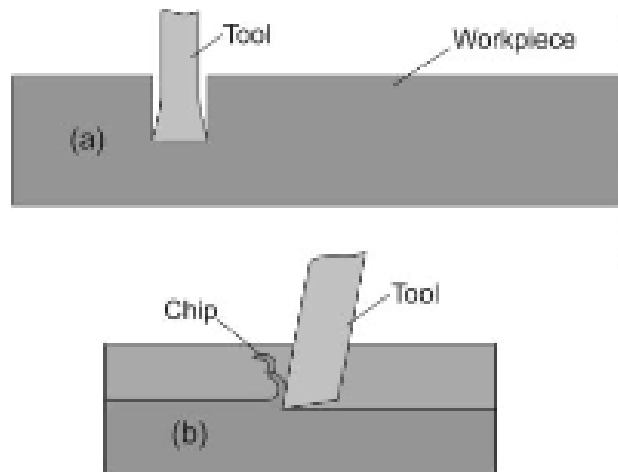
Розташування ріжучого інструменту на дні канавки при операції нарізання торцевої канавки а) формування стружки б) [22]
